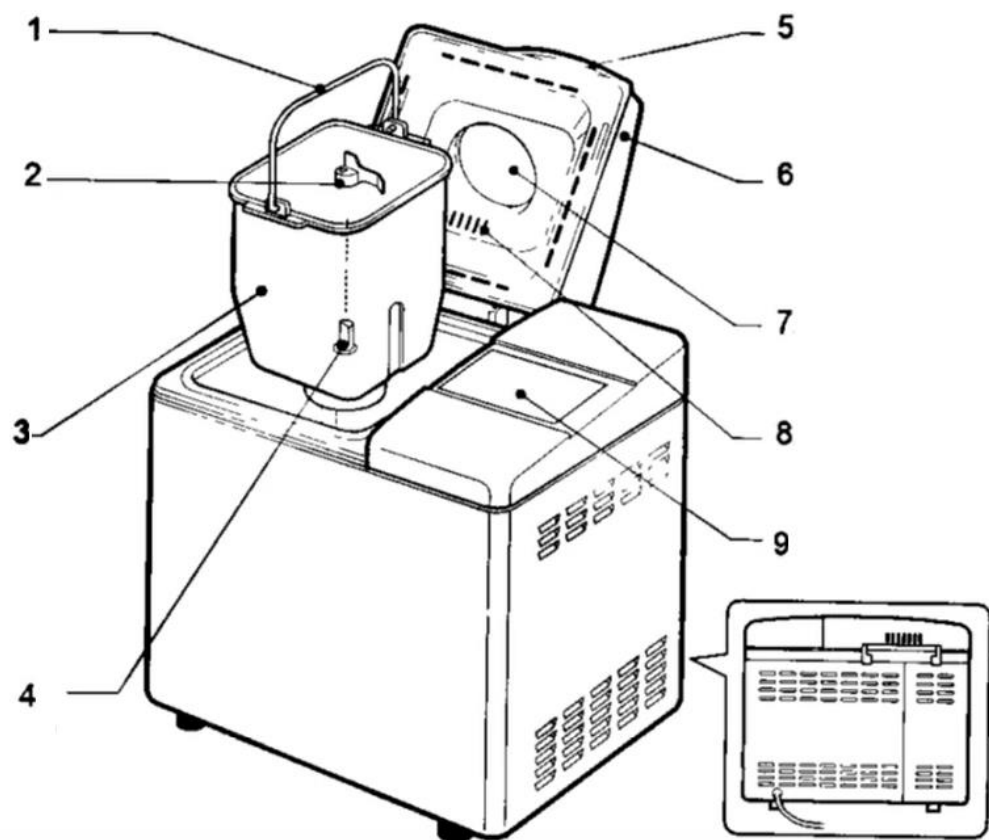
Основні елементи конструкції побутової хлібопічки: 1 – ручка форми; 2 – лопать для замішування тіста; 3 – корпус форми; 4 – шпіндель обертання лопаті; 5 – ручка; 6 – кришка; 7 – оглядове вікно; 8 – вентиляційний отвір; 9 – панель керування
